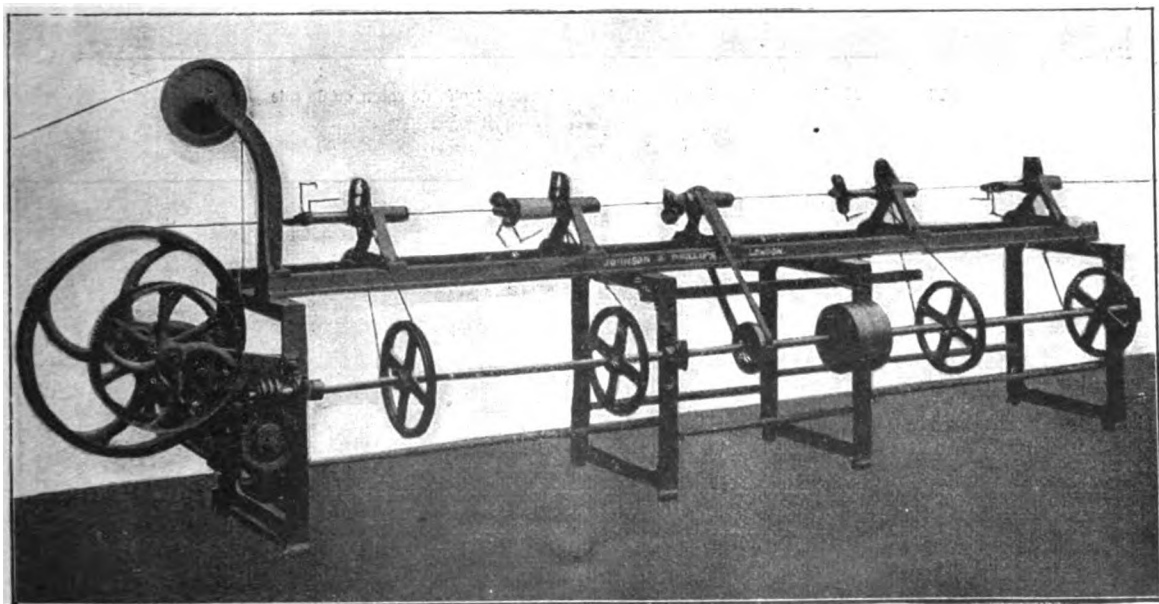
Machine à recouvrir les câbles en une seule opération.
